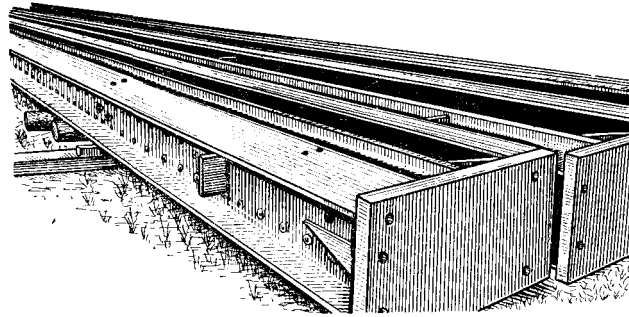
Стойка, сваренная точечной сваркой
